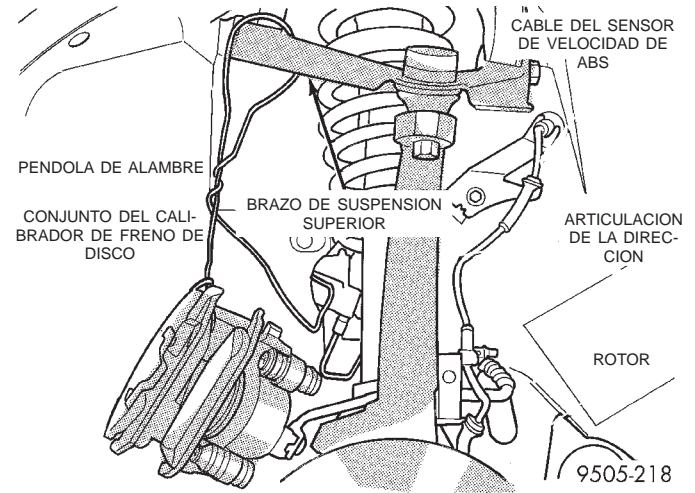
Montaje del calibrador de freno de disco delantero
